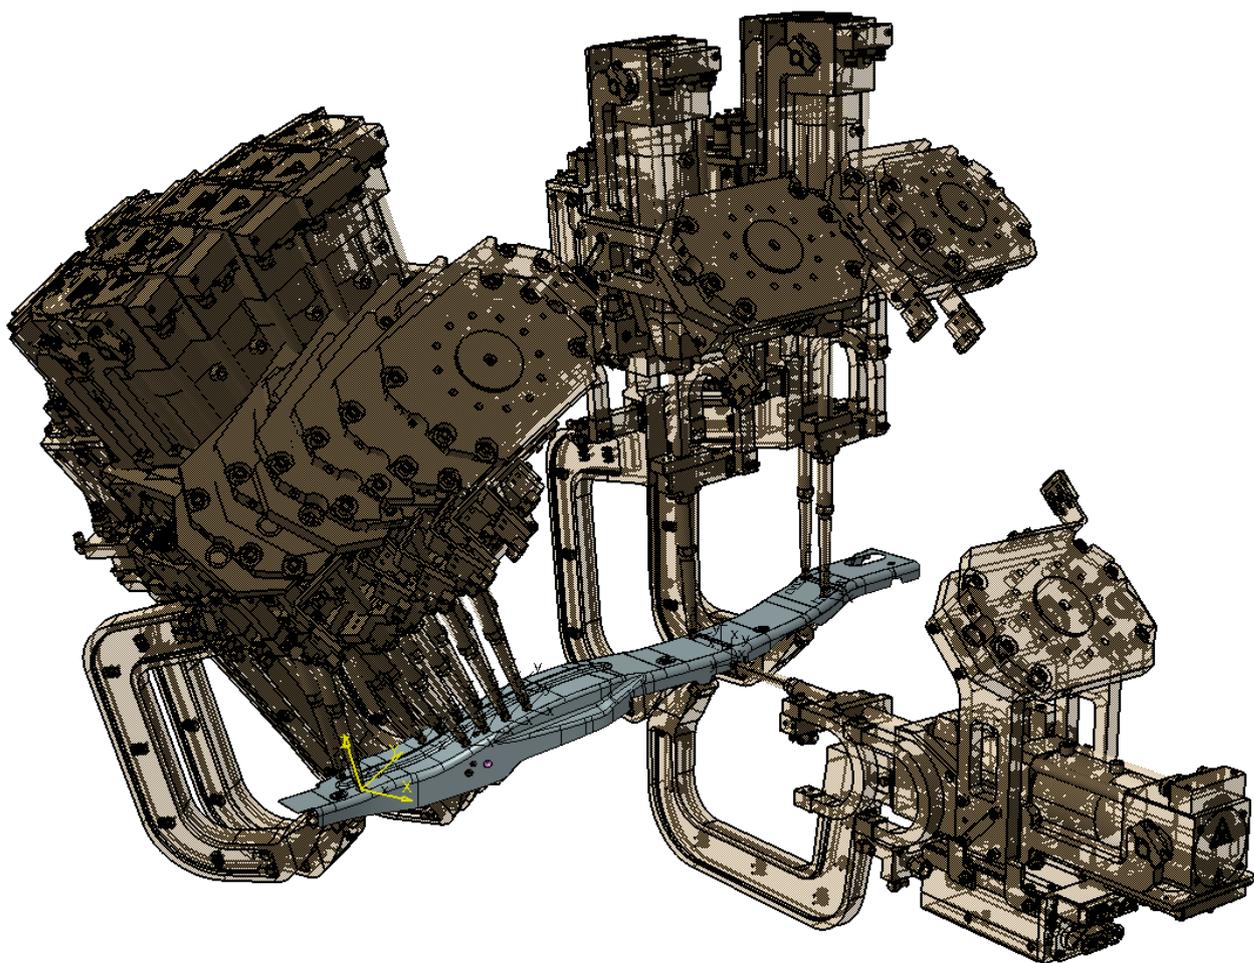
Облако инструмента для сварочной станции
